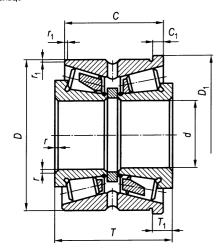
Подшипник роликовый радиально-упорный конический двухрядный с бортом на наружном кольце
